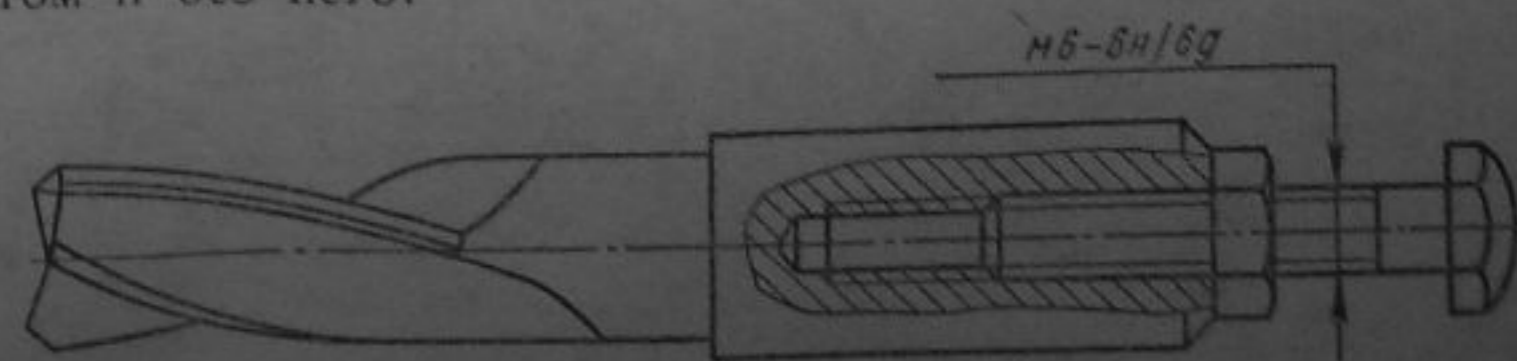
Фреза концевая с регулировочным винтом для настройки вне станка
